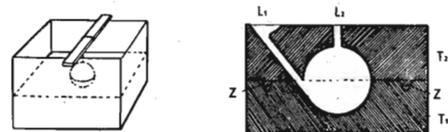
Costruzione di uno stampo per volano. A destra, prospetto e sezione del volano.
